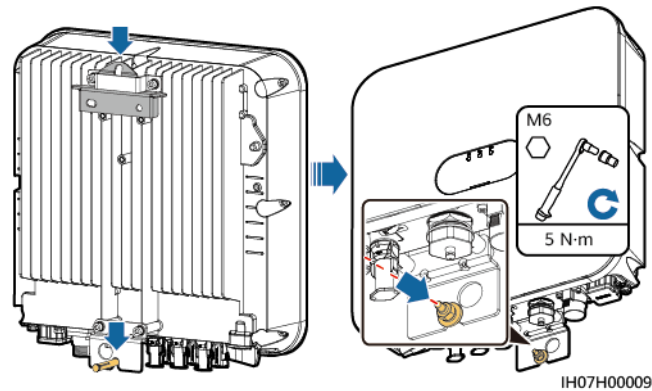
Instalação de um parafuso de travamento na DC switch
